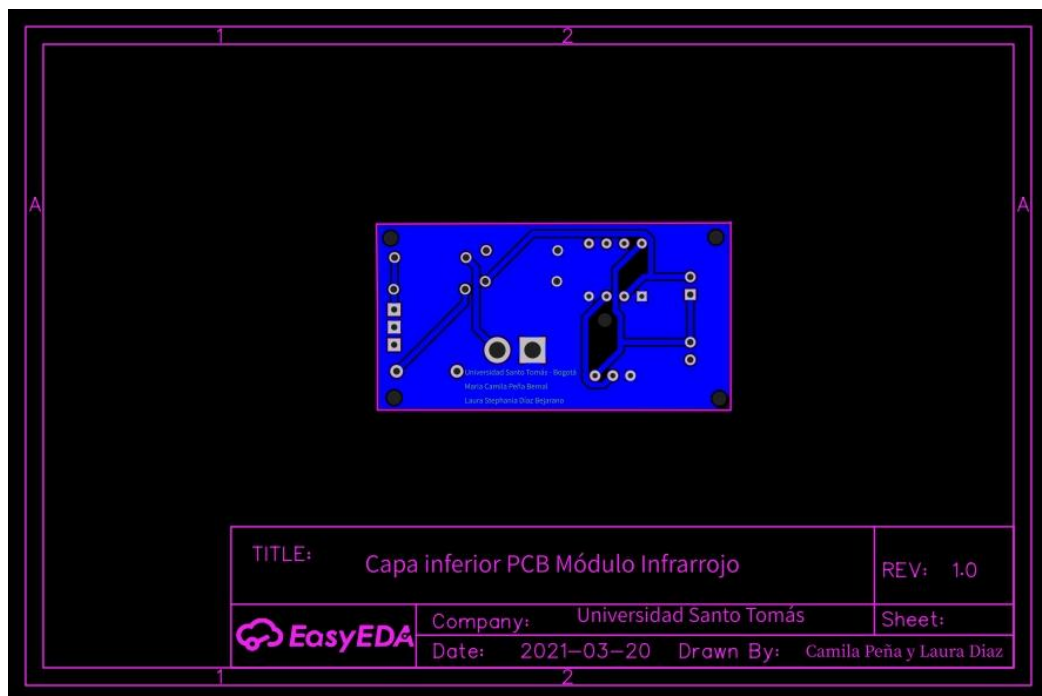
Diseño capa inferior PCB módulo infrarrojo.
